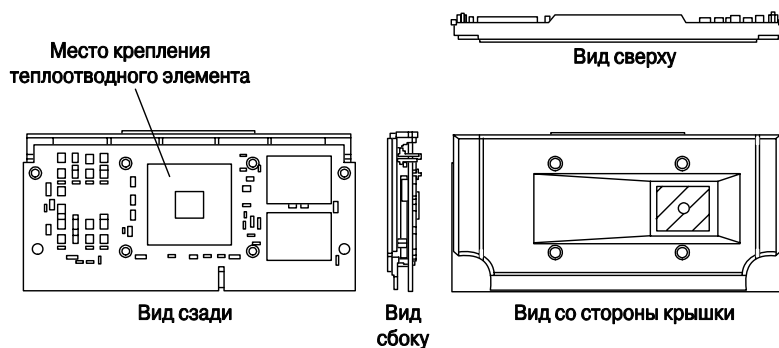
Корпус SECC2 процессоров Pentium II/III
